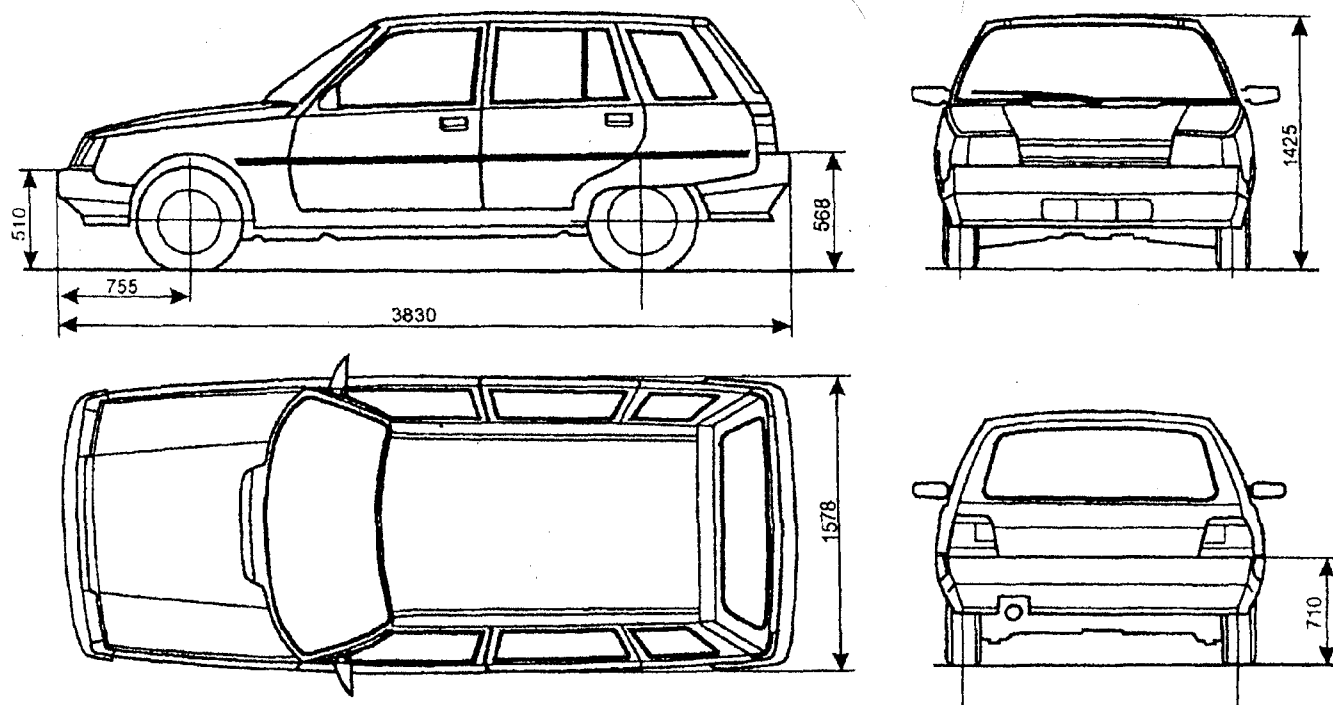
Основные габаритные размеры автомобилей ЗАЗ-1105, ЗАЗ-1125 (высота без нагрузки)
